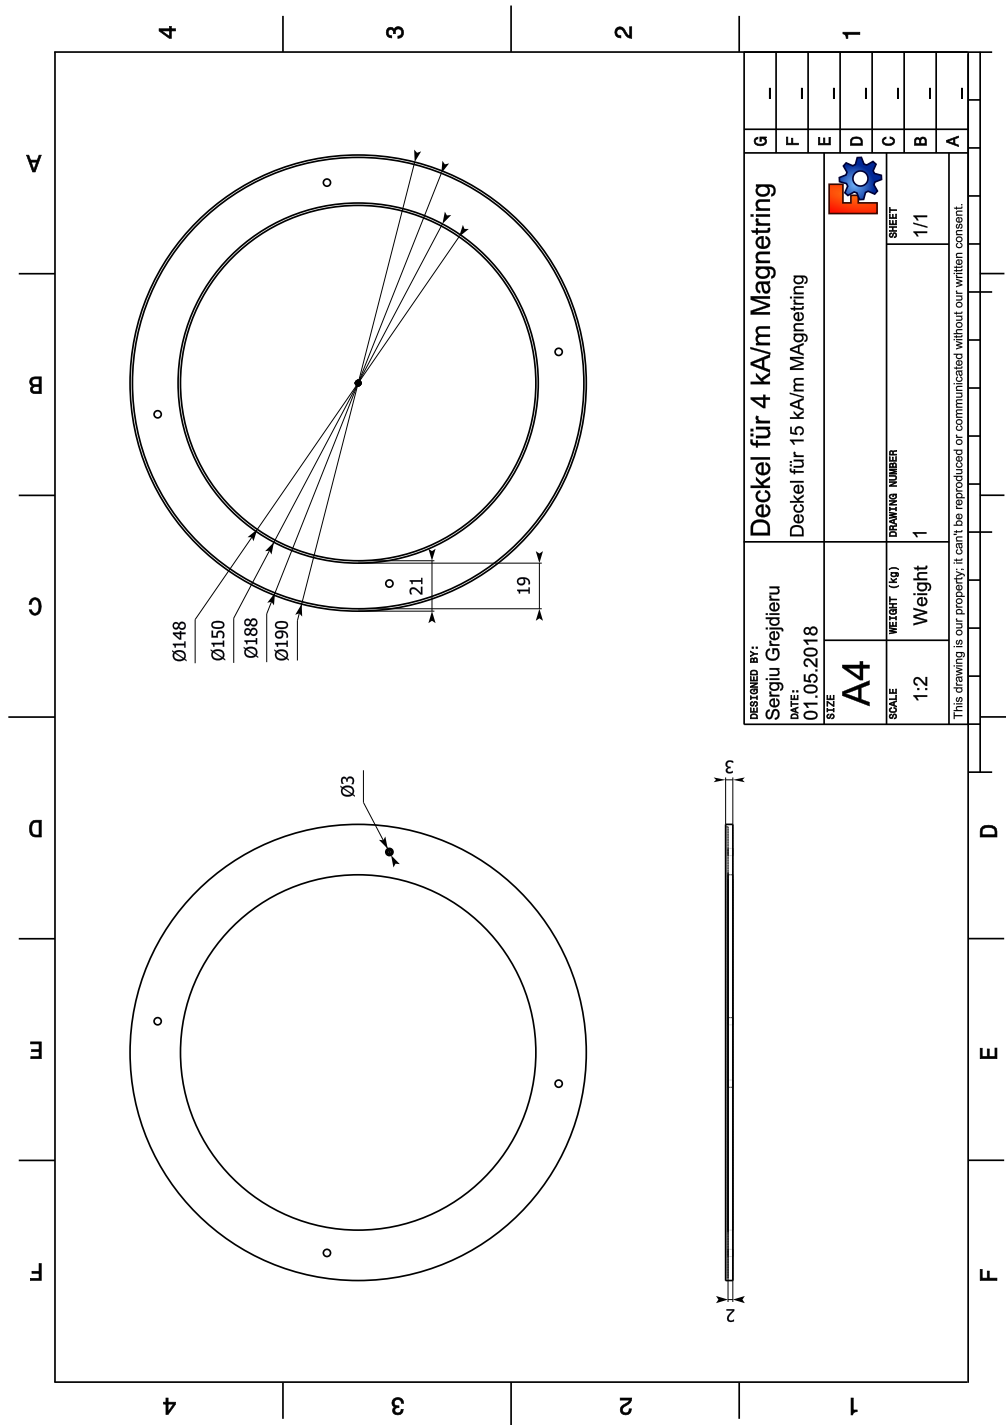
Technische Zeichnung: Deckel für Magnetring 4 kA/m und 15 kA/m
